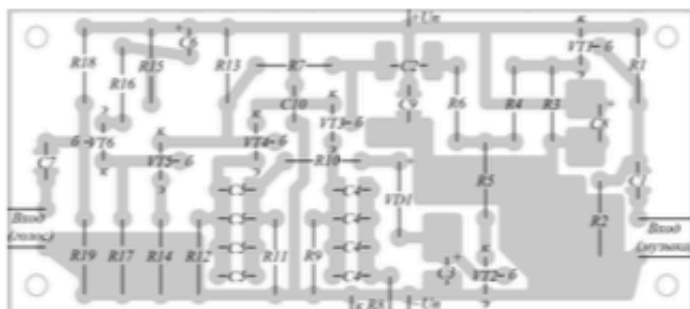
Эскиз расположения деталей на плате микшерного устройства
